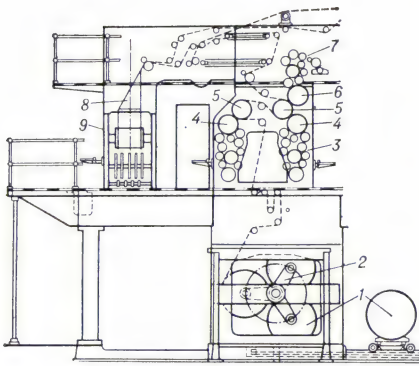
Схема секции газетного агрегата ГАЗУ: 1 — рулон бумаги; 2 — рулонная звезда; 3 — красочный аппарат основной краски; 4 — формный цилиндр основной краски; 5 — печатный цилиндр; 6 — формный цилиндр второй краски; 7 — красочный аппарат второй краски; 8 — воронка; 9 — фальц-аппарат.
